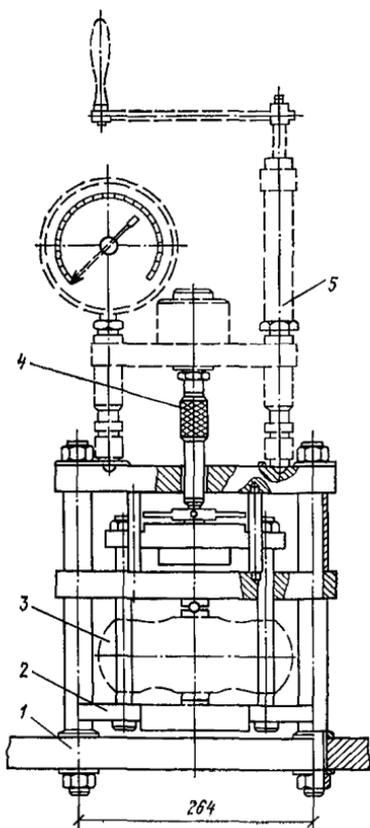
Тарировочное приспособление для прибора типа ГПНВ-5
